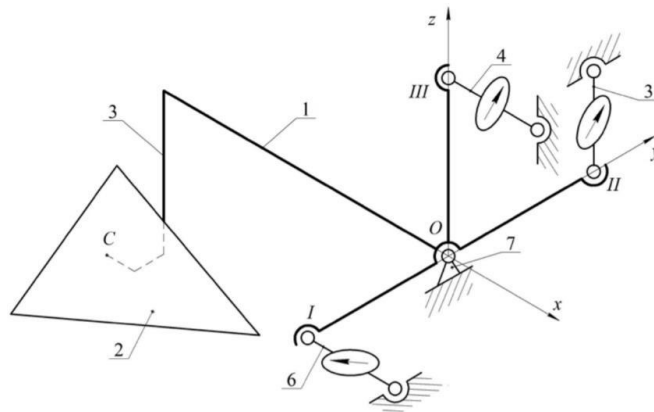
Кінематична схема динамометричного модуля: 1 – корпус динамометричного модуля; 2 – корпус плуга; 3 – стійка корпусу плуга; 4, 5, 6 – динамометри; 7 – сферичний шарнір.
